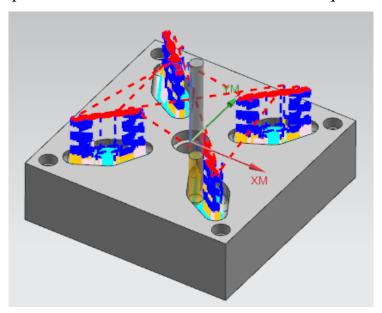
Пример фрезерования колодцев детали «Матрица»
